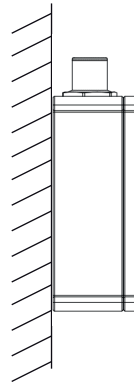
Standard-Befestigungsposition für präziseste Messung ohne Verkipfung des Sensors
